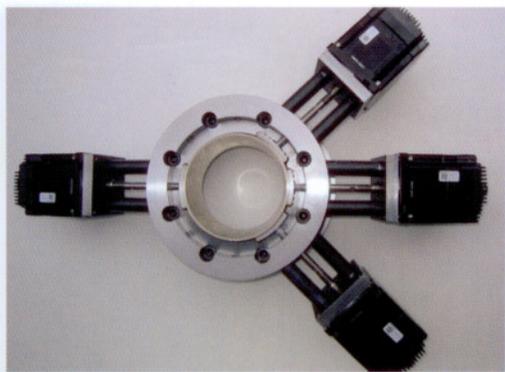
经过改造的模头, 用于 Bobby-Car®。模头由柔性环套 (直径130mm) 与外壳以及四台调节电机组成。 / Fig. 12 Retrofitting kit for the Bobby-Car® head consisting of Flex Ring sleeve (diam. 130 mm) incorporated into an outer housing and four adjusting drives
